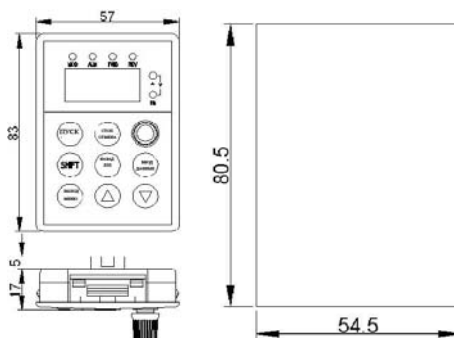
Наружные размеры клавиатуры и ее соединительной коробки
